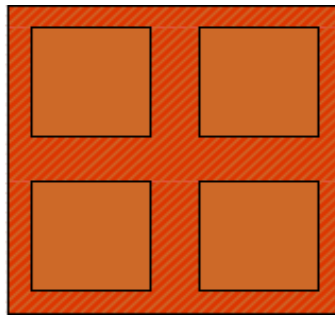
Prototipo de las figuras geométricas que se realizan con la cortadora láser
